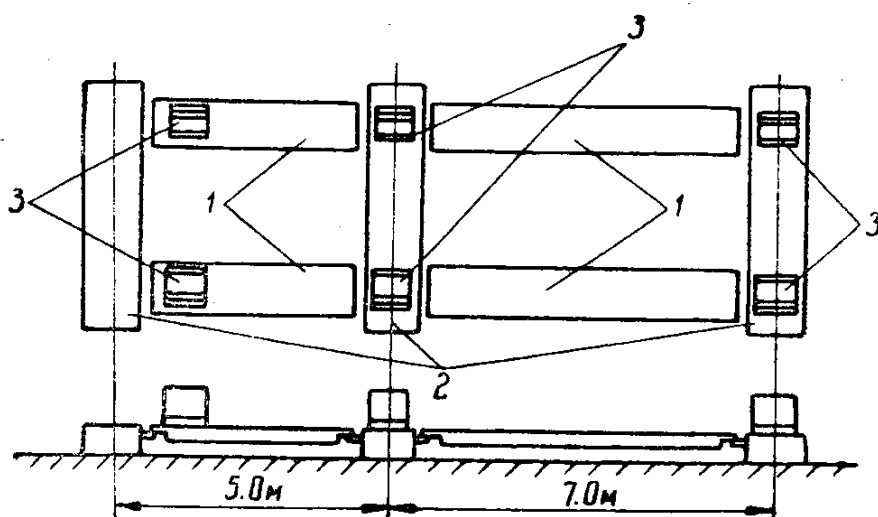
Схема объемного кондуктора: 1 — подвижные балки; 2 — стационарные разметочные плиты; 3 — тумбочки со втулками и упорами.
